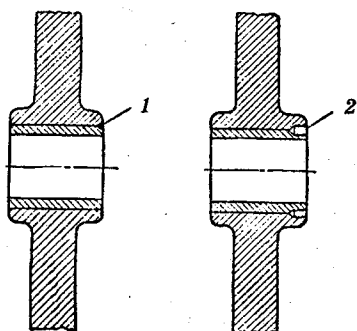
Постановка втулки в гнездо под наружную обойму шарикового или роликового подшипника:
